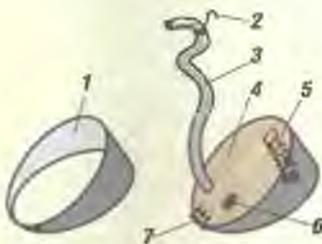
Насос: 1 — сегмент камеры; 2 — крючок для подвешивания на улей; 3 — шланг; 4 — верхняя пластина; 5 — пружина; 6 — обратный клапан; 7 — форточная петля
